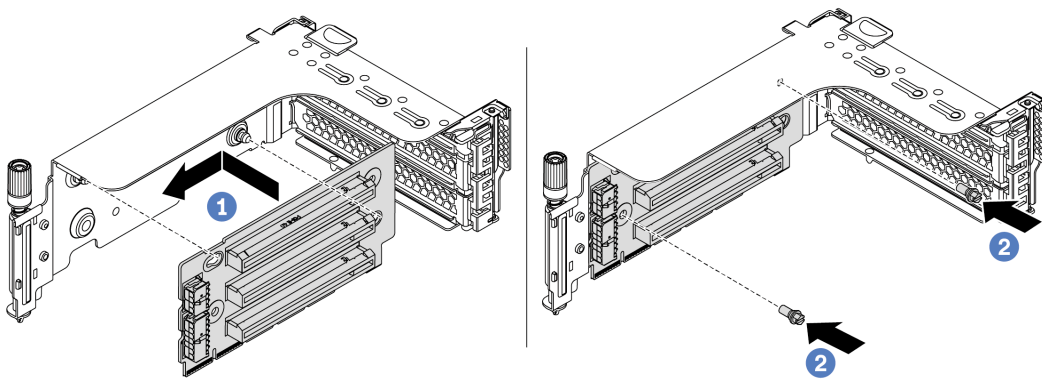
Installazione della scheda verticale (staffa verticale a tre slot)
